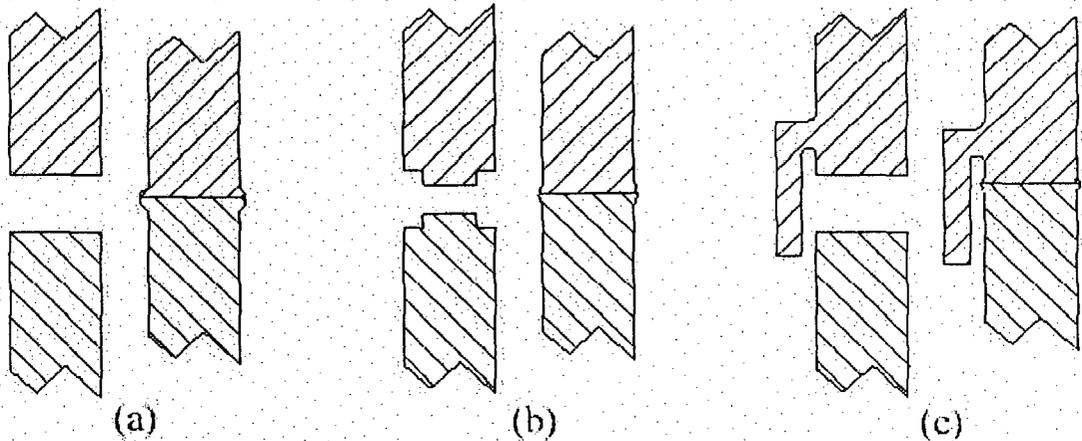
Uniões para soldagem por ferramenta aquecida.
